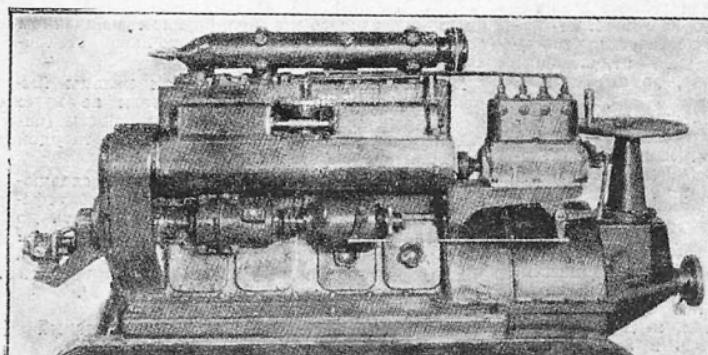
Общий вид дизельного двигателя „Вайземан“ с левой стороны
